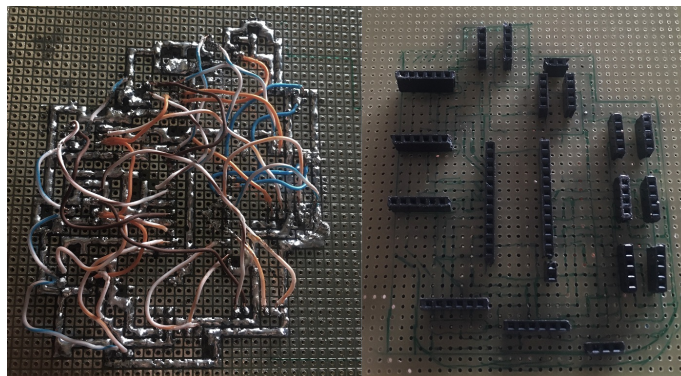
Soldadura del circuito para Dextra TPMG90-2.
